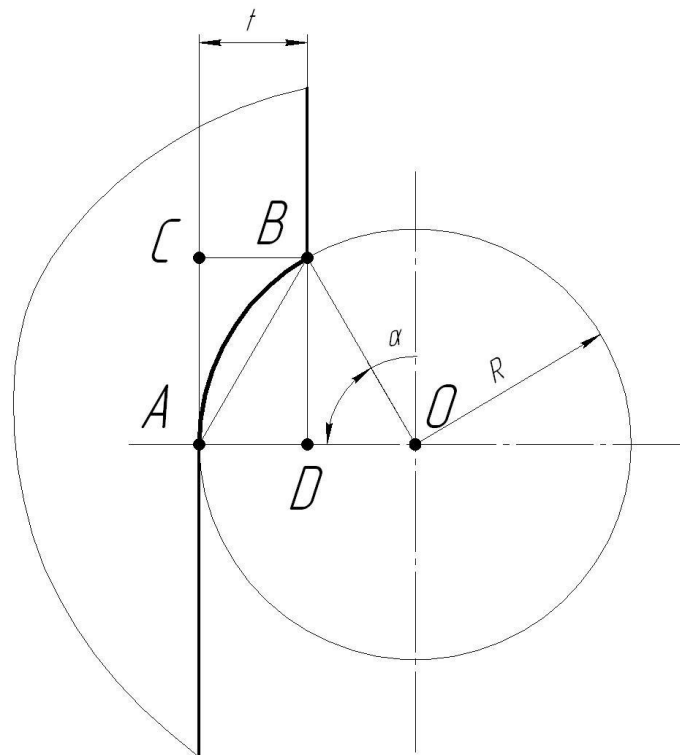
Схема обробки прямолінійної ділянки пуансона кінцевої фрезою діаметром R з припуском t
